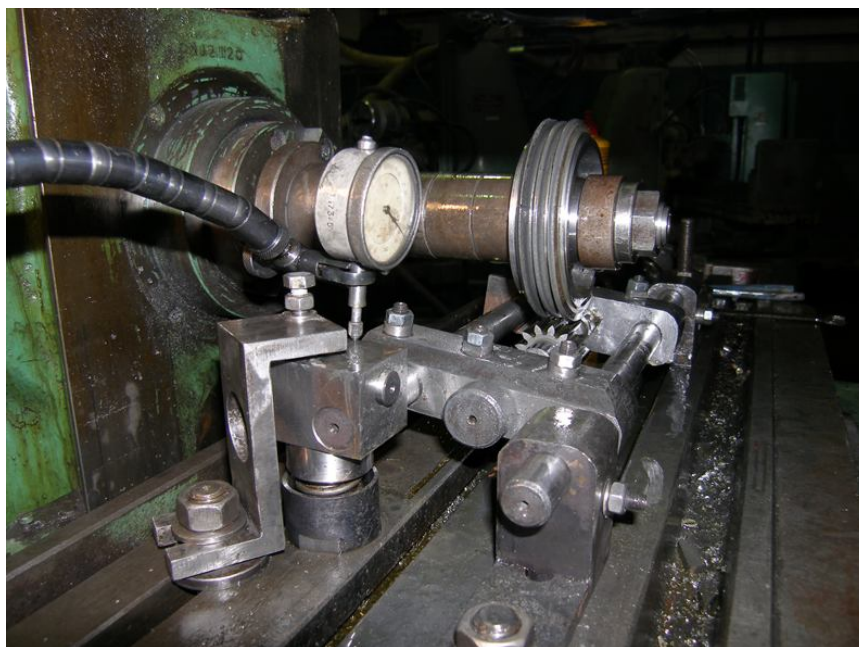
Общий вид рабочей зоны зубохонингования
